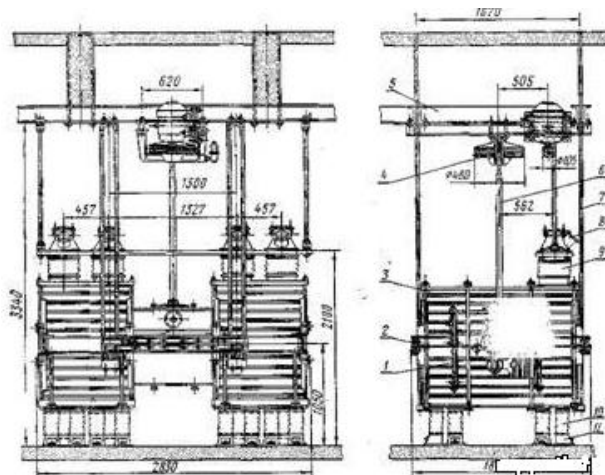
Рассев ЗРМ: 1 — балансирующий механизм; 2 — главная рама; 3 — ситовой корпус; 4 — верхняя подвеска; 5 — металлическая рама; 6 — веретено; 7 — трос; 8 — приемная аспирационная коробка; 9 — приемный рукав; 10 — выпускной рукав; 11 — выпускной патрубок
